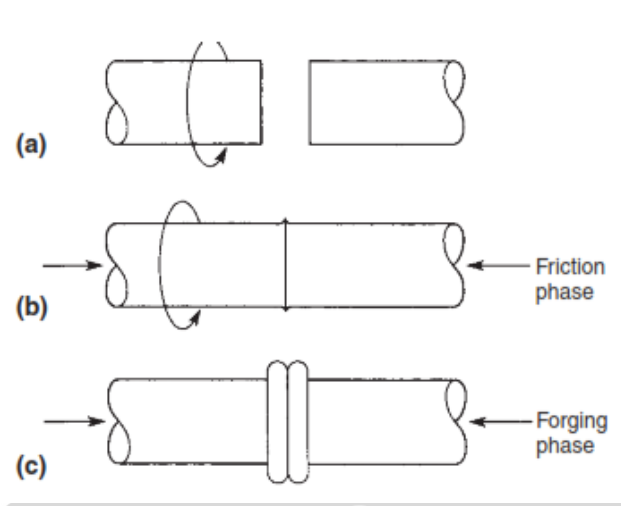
Simulasi *Linier Friction Welding
